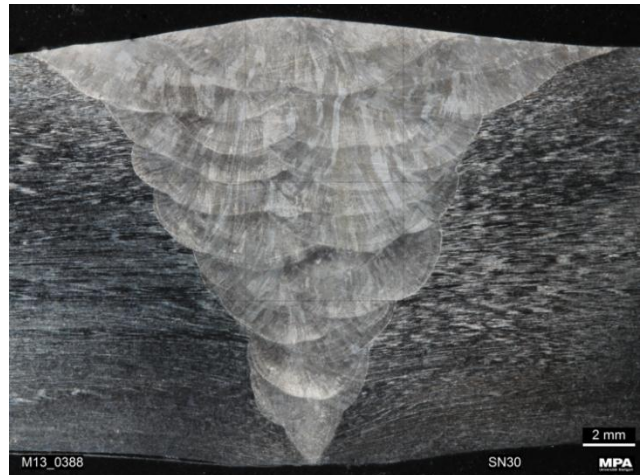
Schweißnaht mit mechanischer Behandlung nach dem Erstarren jeder einzelnen geschweißten Raupe mit Hilfe eines Pressluftmeißels
